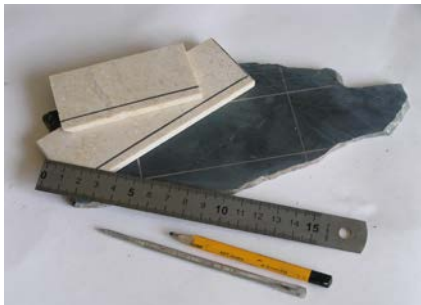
Разметка заготовок. Рис. 101. Резка пластин на заготовки
